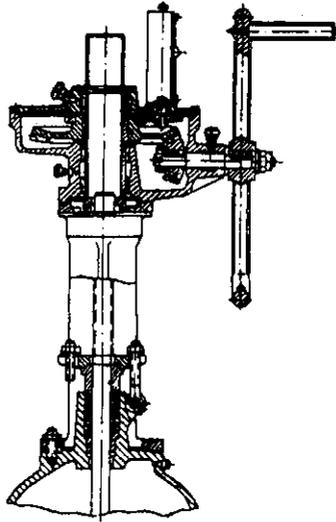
Редуктор для ручного управления с зубчатой конической передачей для правой ходовой резьбы
